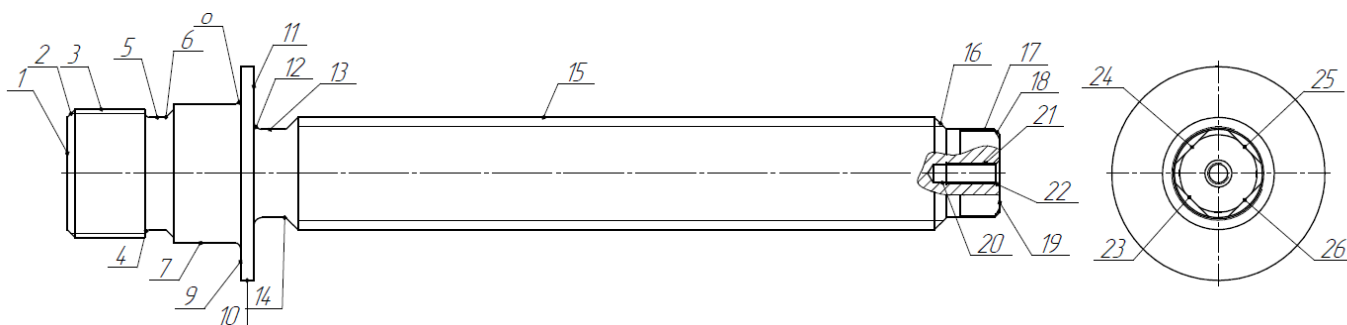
Ескіз деталі гвинт натискний з нумерацією поверхонь
